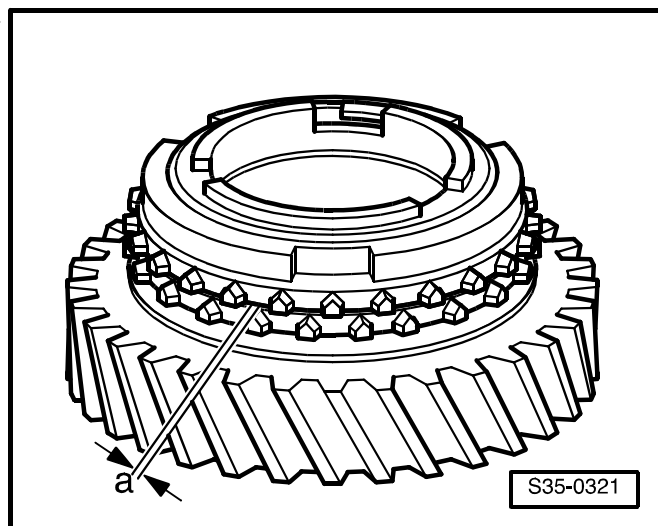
Положение для сборки наружной обоймы (кольца), внутреннего кольца и блокирующего кольца синхронизатора для 2-ой передачи
